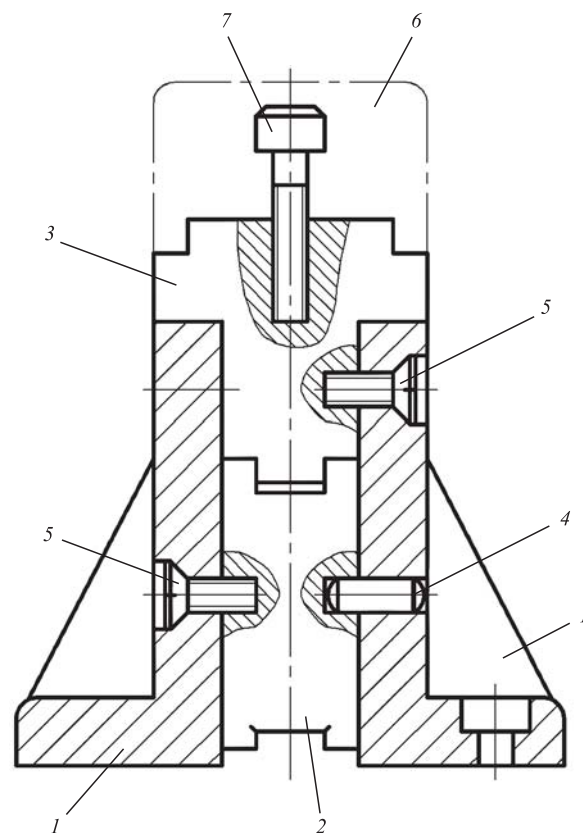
Сборно-модульная конструкция корпуса линейной протяжки
